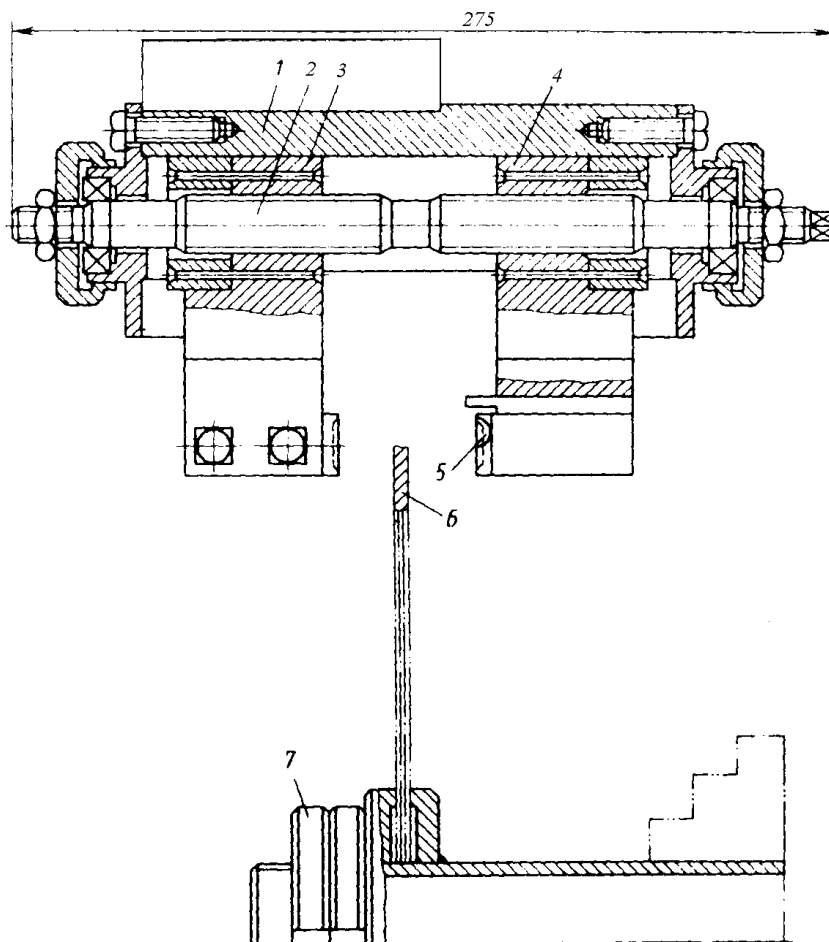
Приспособление для изготовления гребенчатых прокладок.
